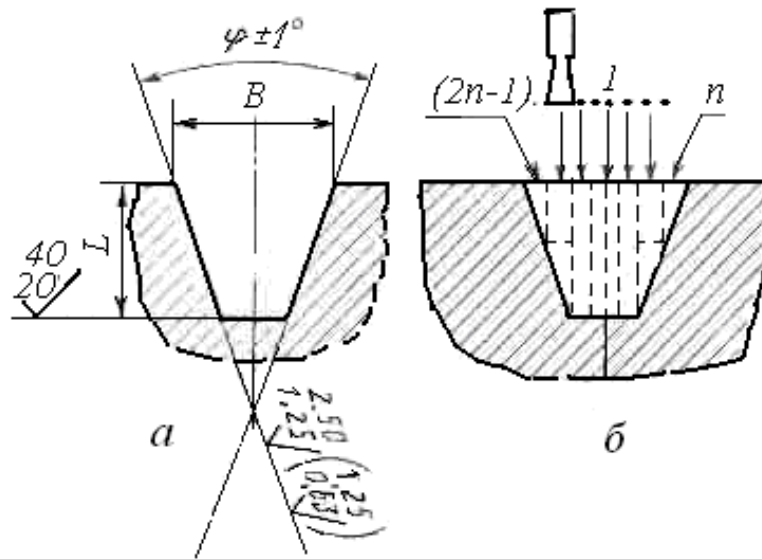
Схемы перемещения инструмента при обработке канавки шкива канавочным резцом: *a* – форма канавки; *б* – перемещение резца
